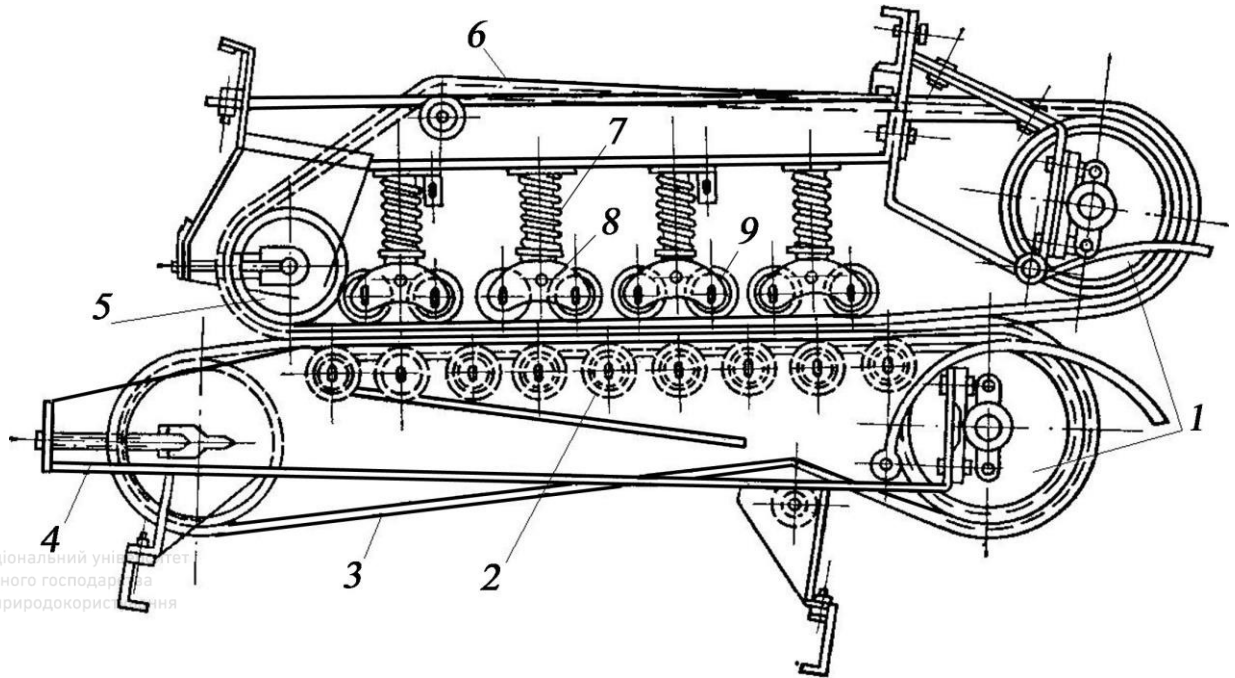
Затискний транспортер: 1 - ведучі шків; 2 - підтримуючий ролик; 3 - пас нижньої секції; 4 - натяжний пристрій; 5 - ведений шків; 6 - пас верхньої секції; 7 - пружина; 8 - каретка притиска; 9 - ролик каретки.
